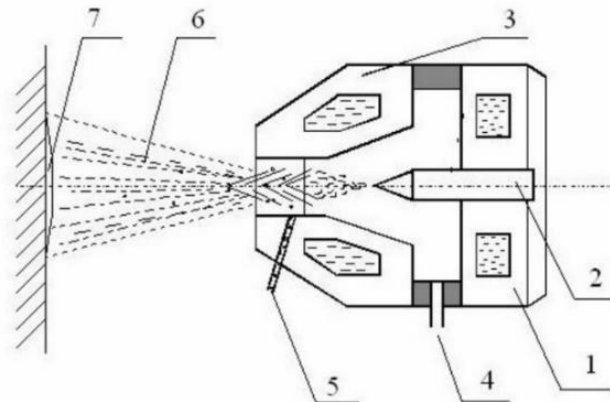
Схема плазменно-порошкового напыления: 1 - корпус плазмотрона; 2 - катод (вольфрамовый электрод); 2 - катод (охлаждаемое сопло); 4 - канал подачи плазмообразующего газа; 5 - инжектор для подачи порошка; 7 - подложка (напыляемая поверхность)
